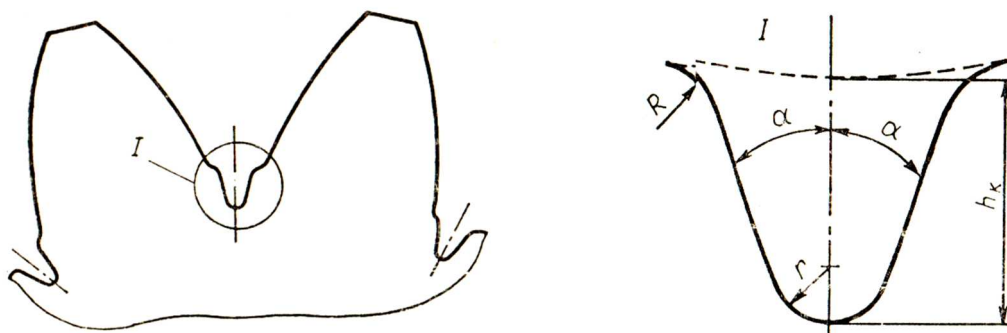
Зубчатое колесо с искусственными концентраторами во впадинах
